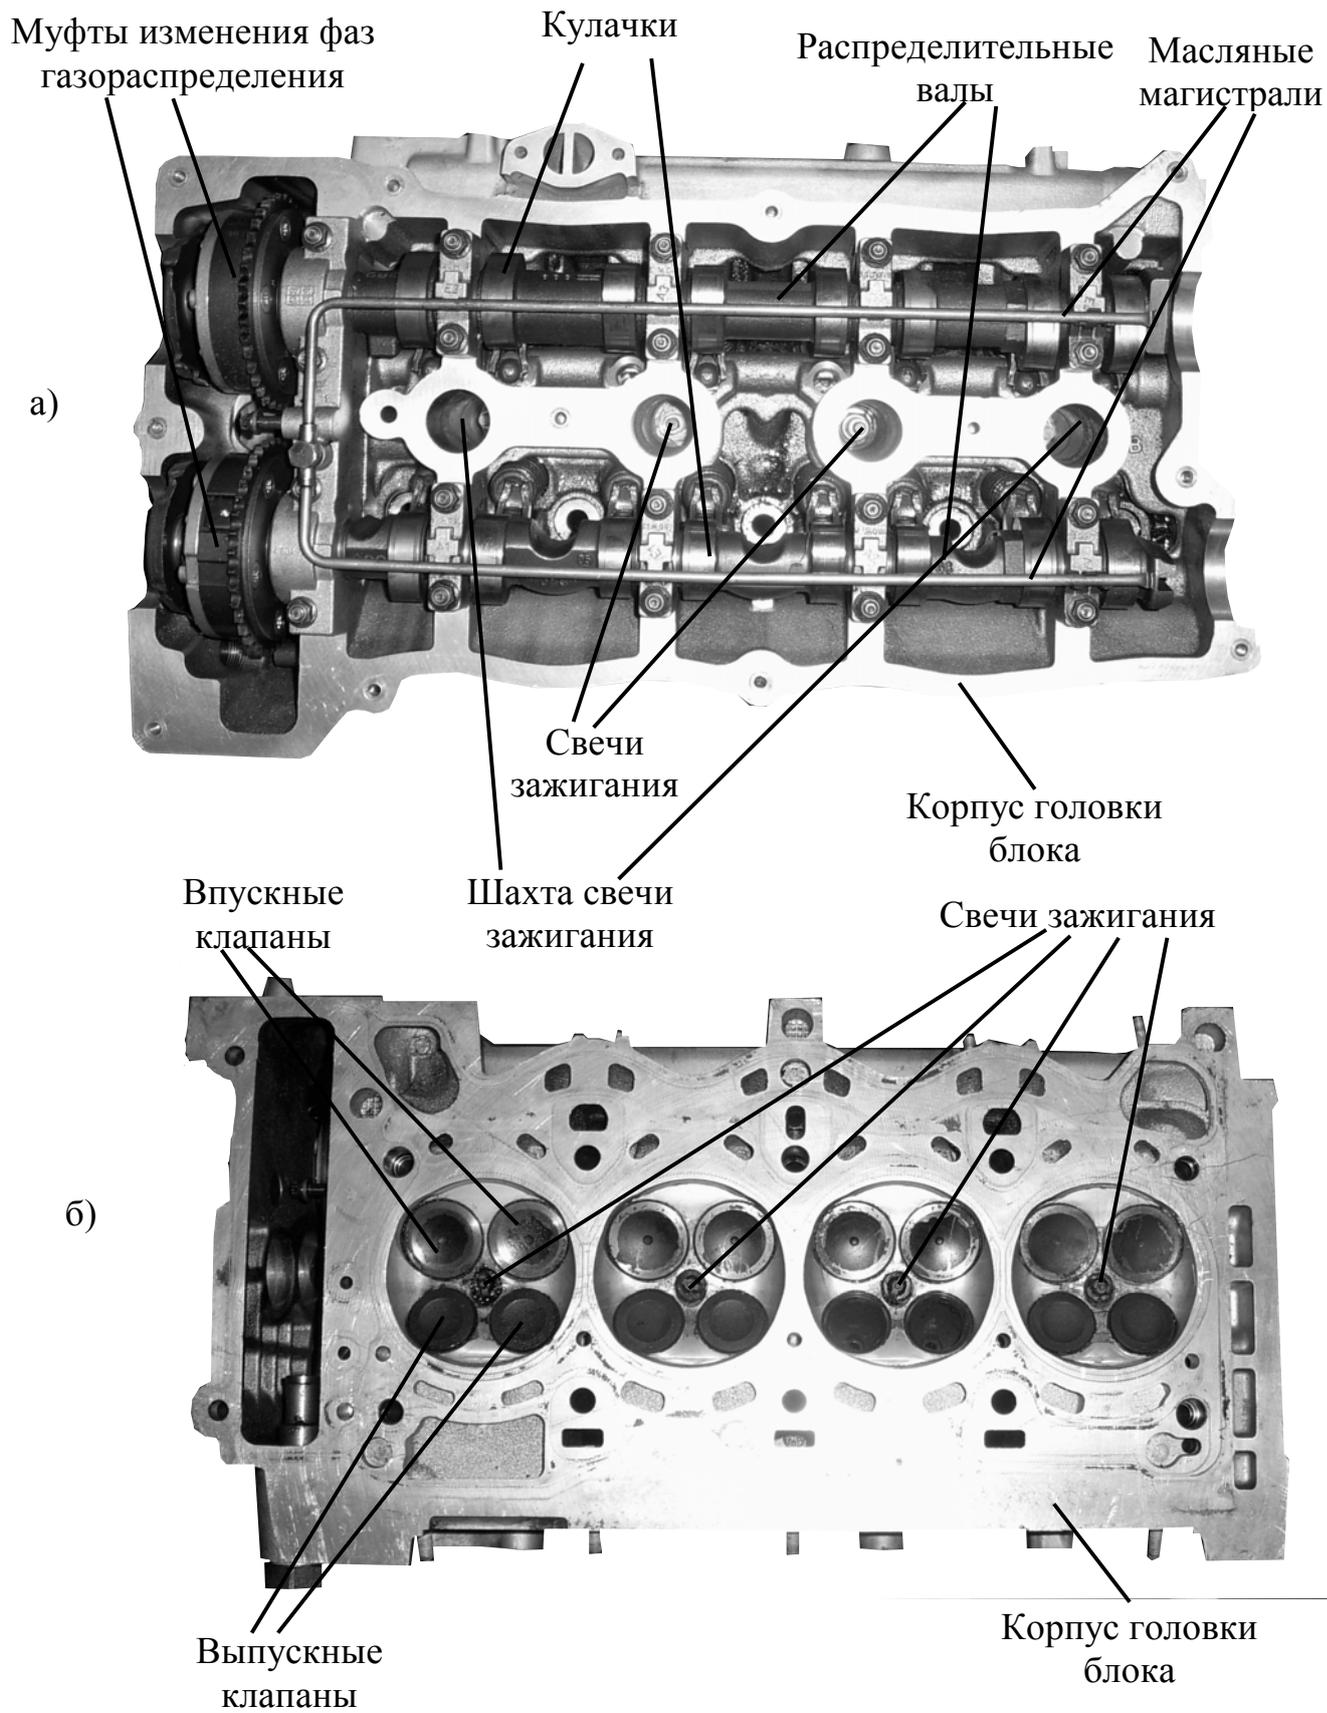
Головка блока цилиндров: а) вид сверху, б) вид снизу
